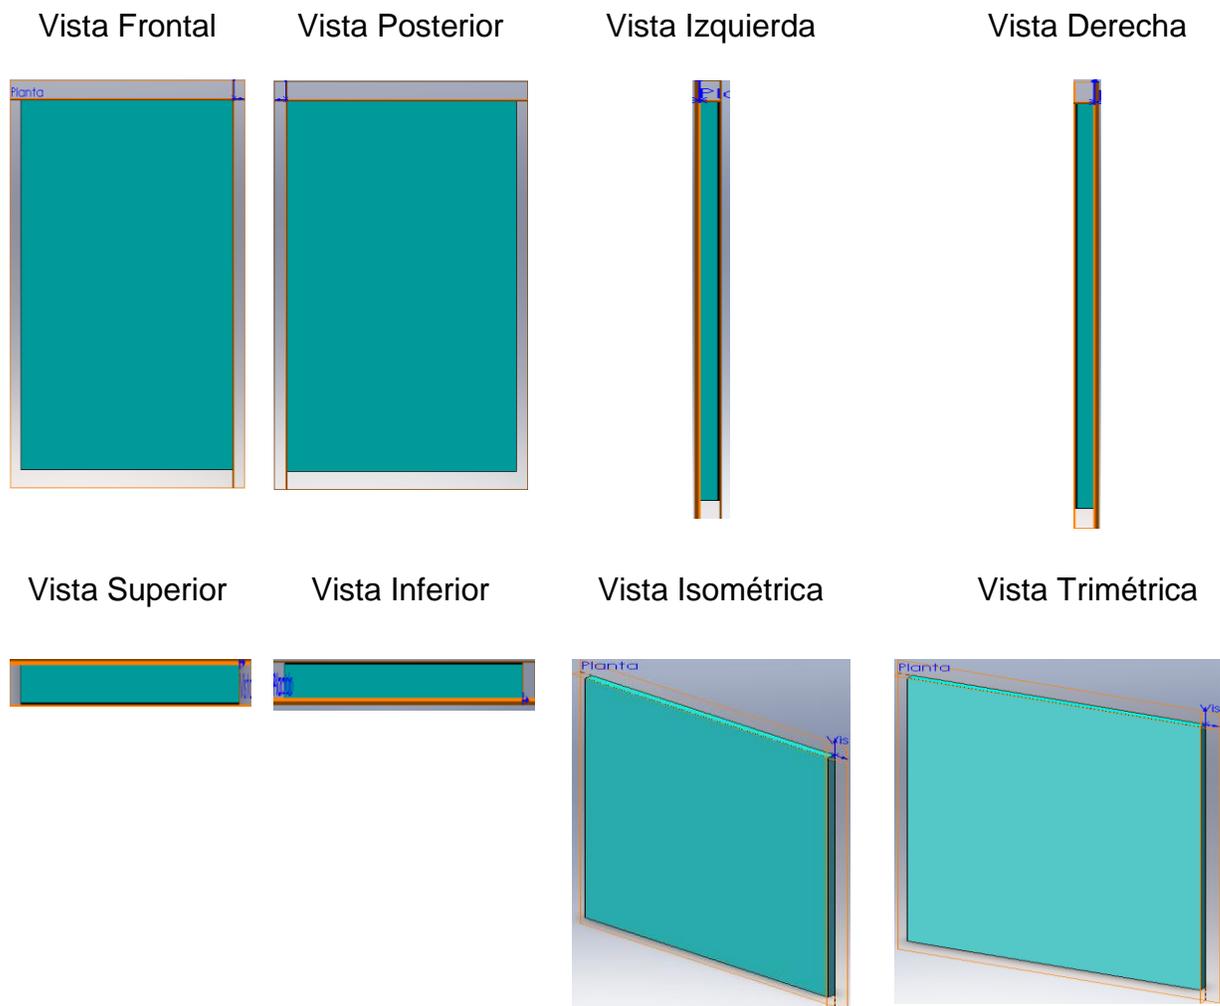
Vistas de la placa lateral izquierda. Fuente de autor
